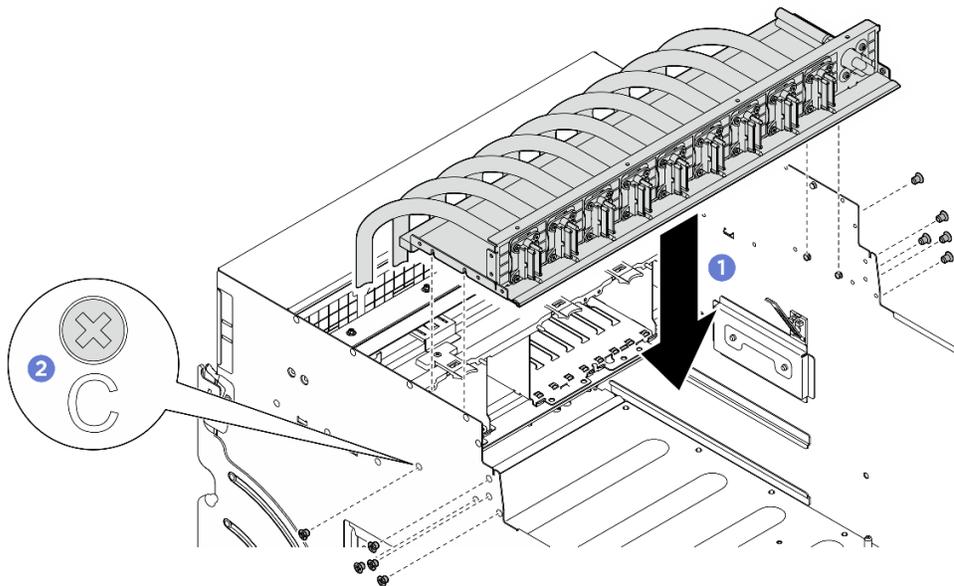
Instalación del Arnés de cables del conmutador PCIe frontal
